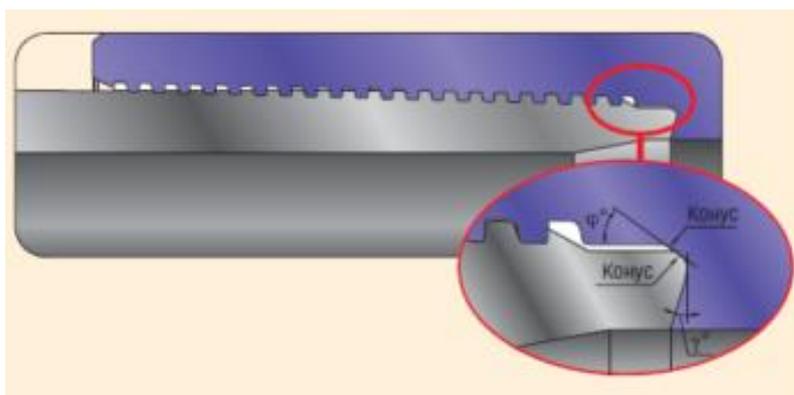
Конструкция резьбового соединения ТМК FMT:
